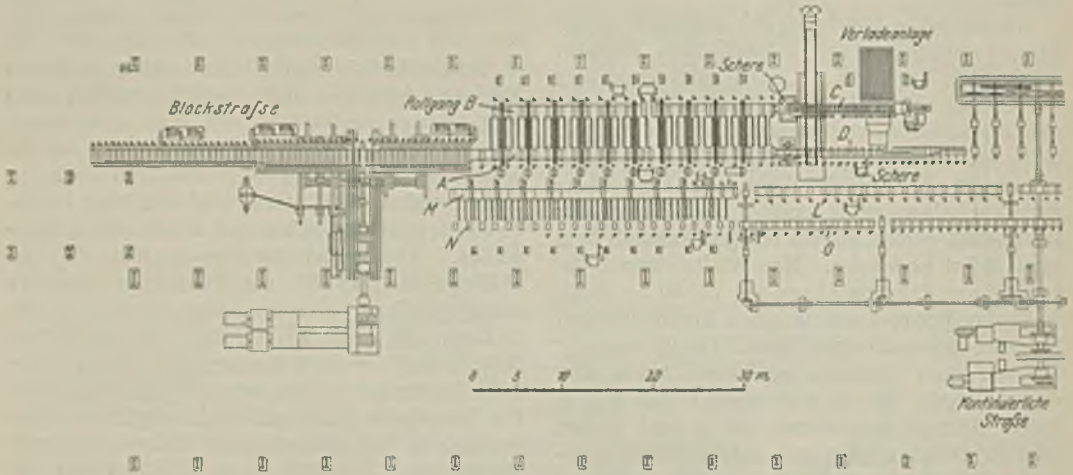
Walzwerksanlagen der Brier Hill Steel Co.
